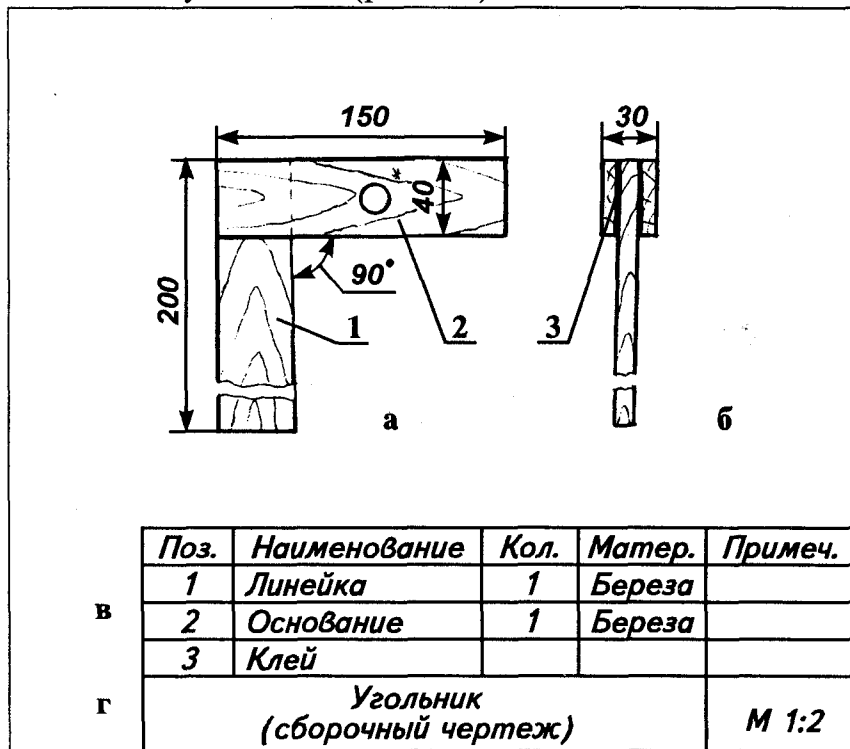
Сборочный чертеж угольника: а — главный вид; б — вид слева; в — спецификация; г — основная надпись
